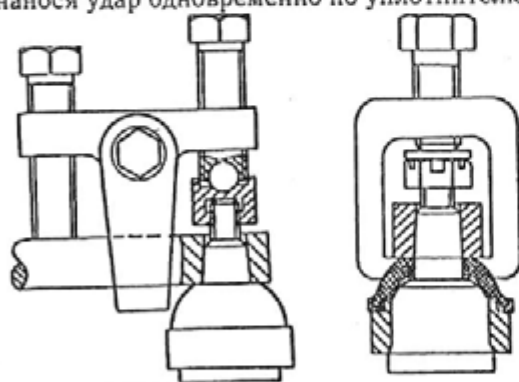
Выпрессовка пальца шарового шарнира рулевых тяг:
